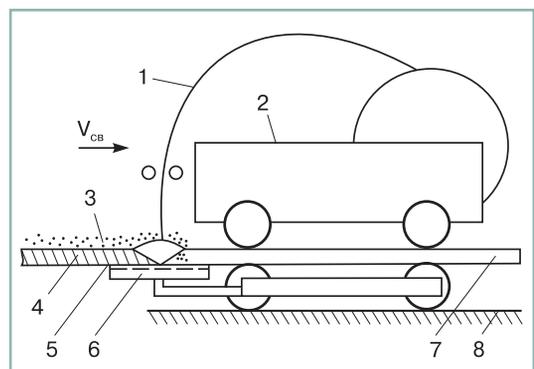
Схема односторонней автоматической сварки с автономным перемещением ползуна: 1 — сварочная проволока; 2 — сварочный автомат; 3 — флюс; 4 — шов; 5 — шлак; 6 — медный ползун; 7 — свариваемый металл; 8 — направляющая
